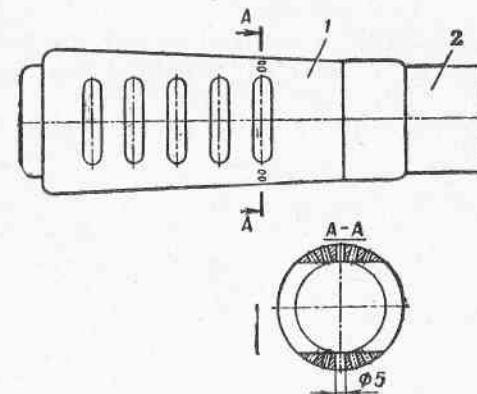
Подготовка дульного тормоза к отрезке (сверление отверстий для отрезки по окружности):
